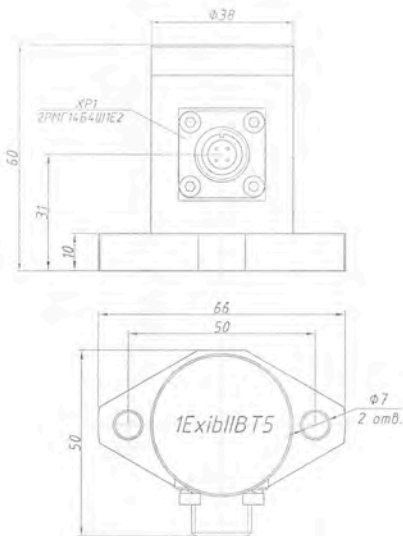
Габаритные и установочные размеры ИД-40.00-2
